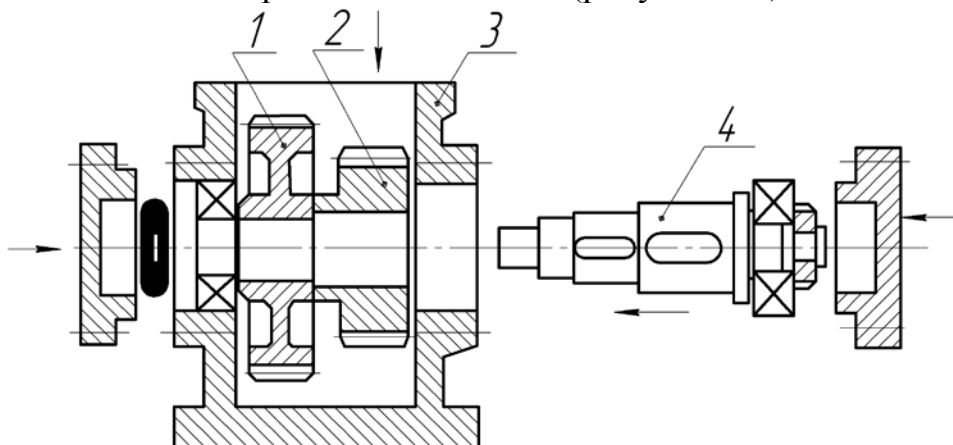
Схема осевой сборки промежуточного вала двухступенчатого редуктора с продеванием вала через введенные в корпус сверху зубчатые колеса: 1, 2 – зубчатые колеса; 3 – корпус; 4 – вал
